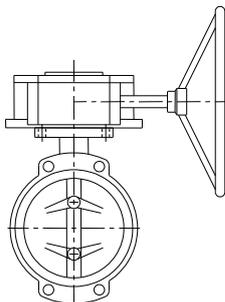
Riduttore sinistrorso montato perpendicolarmente alla valvola
